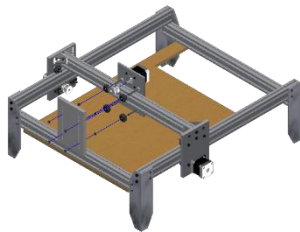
Y-Axis Assembly Moves Tool* (Sumber: Penelitian)
